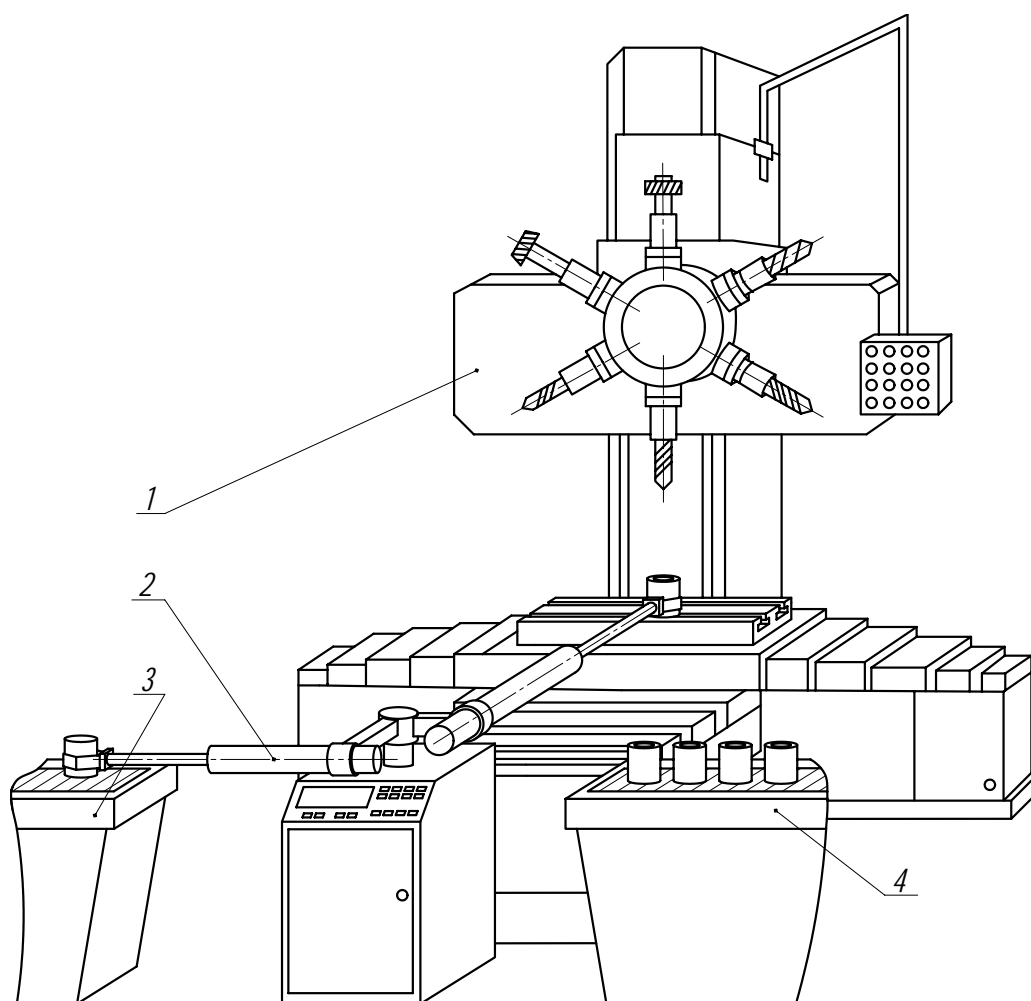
Свердлильний роботизований технологічний комплекс:
